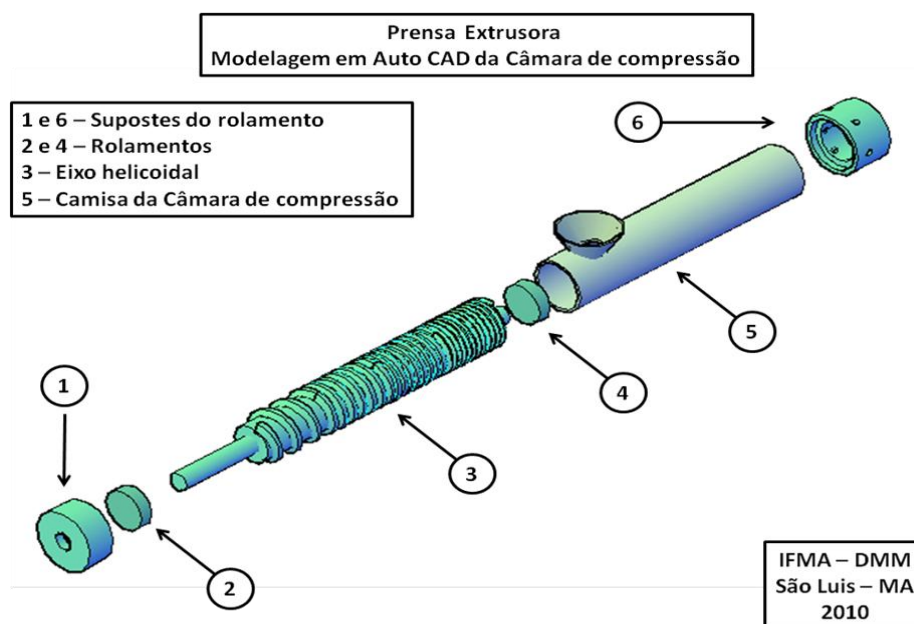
Modelagem em CAD da câmara cilíndrica de compressão do protótipo da prensa extrusora.
